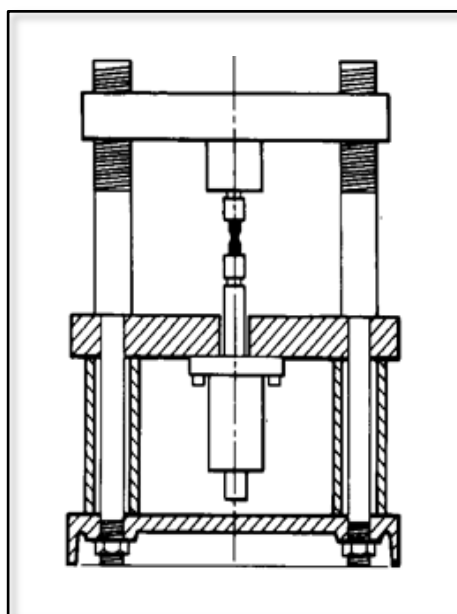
Esquema del tren de carga en una máquina de fatiga axial electrohidráulica [50].
